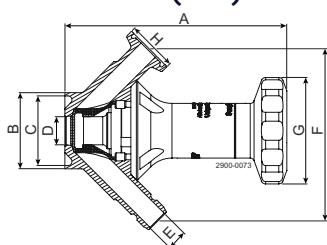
Poignée avec corps de vanne : Tuyau à collet à souder
